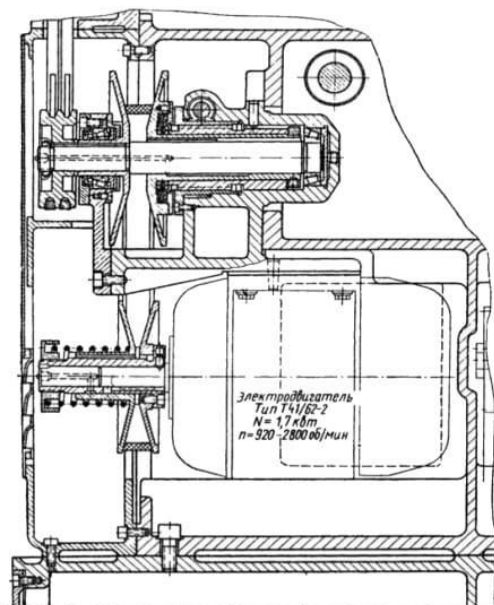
Продольный разрез вариатора, встроенного в привод главного движения зубофрезерного станка 5K301.
